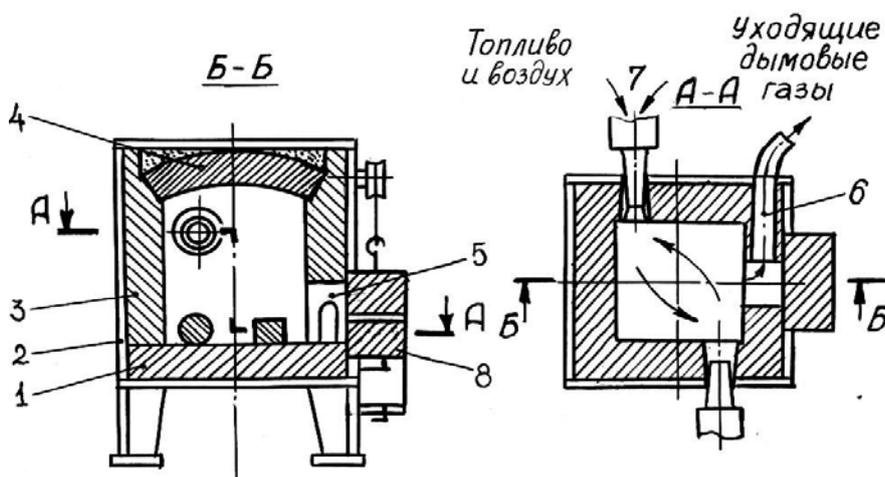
Схема камерной печи: 1 – под; 2 – кожух; 3 – стенки; 4 – свод; 5 – окно; 6 – канал; 7 – форсунки; 8 – заслонка
